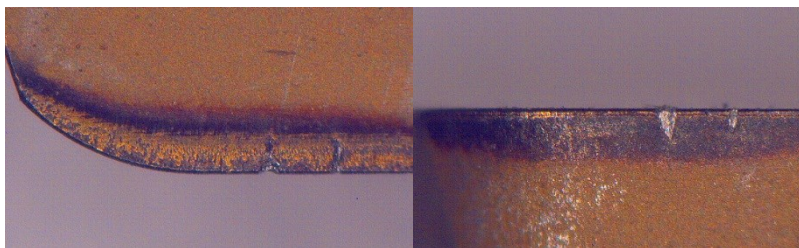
Tepelné hřbenové trhliny vzorku č. 1 po prvním průjezdu
